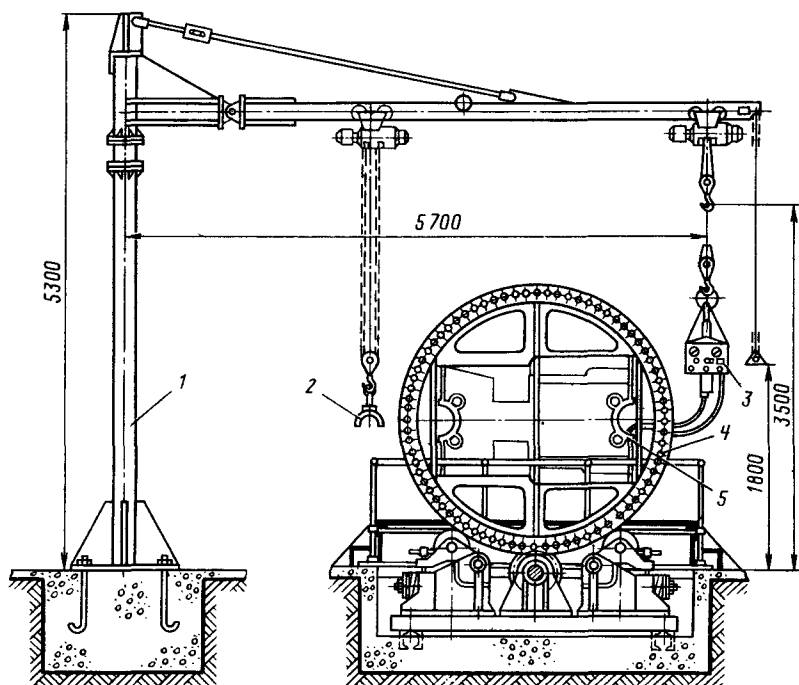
Стенд-кантователь для дефектоскопии и сварки блока дизеля типа Д100:
